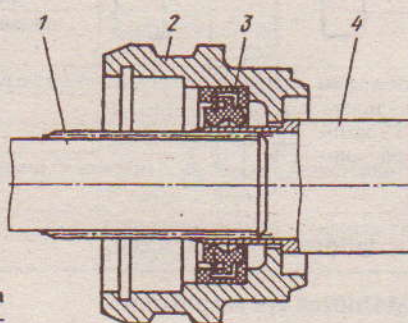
Приспособление, предохраняющее манжету от повреждения: 1 - полуось; 2 - корпус; 3 - манжета; 4 - оправка
